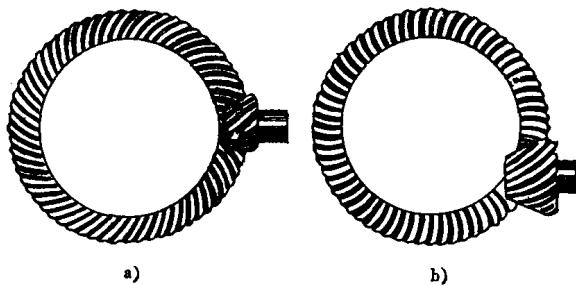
10 主、从动齿轮齿数分别相同的螺旋锥齿轮和双曲面齿轮的比较
